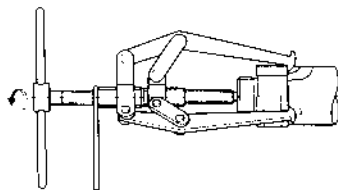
Канавки в корпусе конического роликоподшипника для установки съемника
